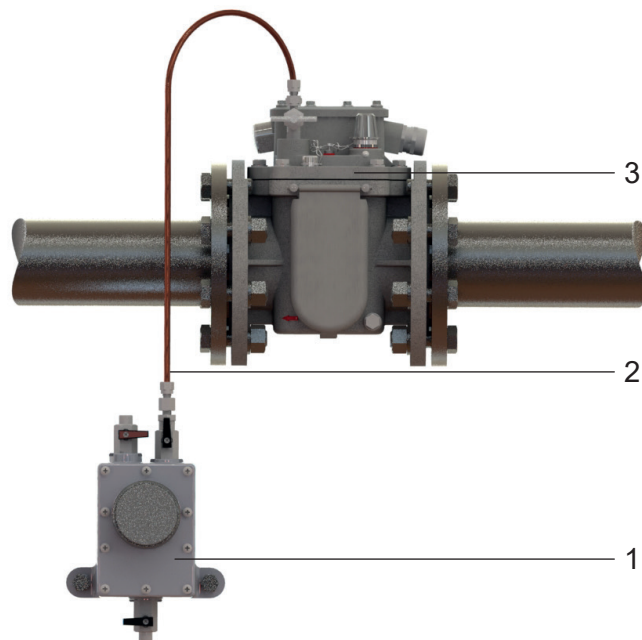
Установка газоотборного устройства ZG 1.2.
